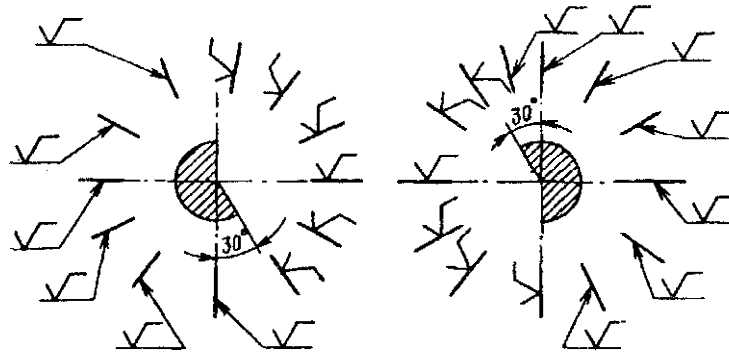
Варианты расположения знака обозначения шероховатости с полкой
